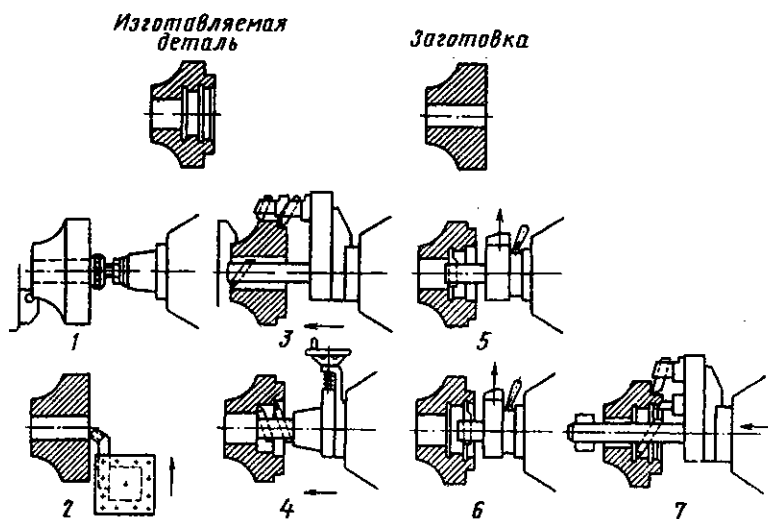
Схема обработки детали на токарно-револьверном станке с вертикальной осью вращения револьверной головки:
